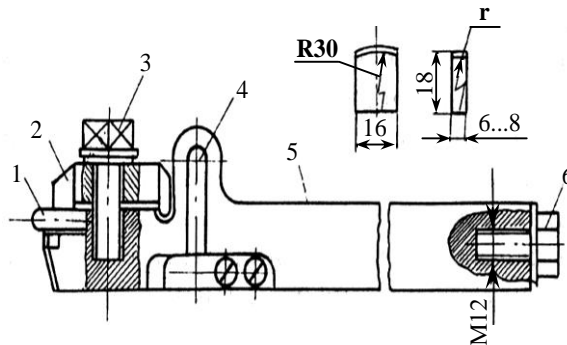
Пружинна державка з інструментом у вигляді пластини:
